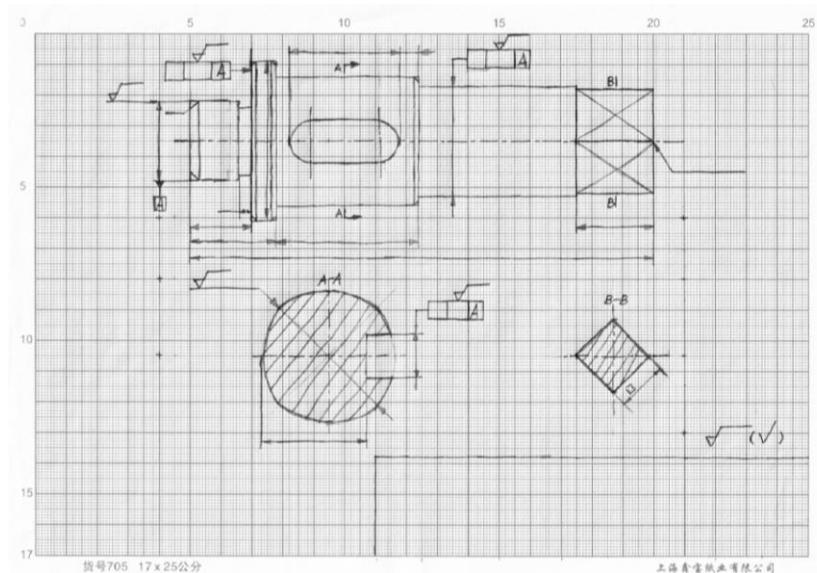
画出尺寸线、箭头和形位公差框
